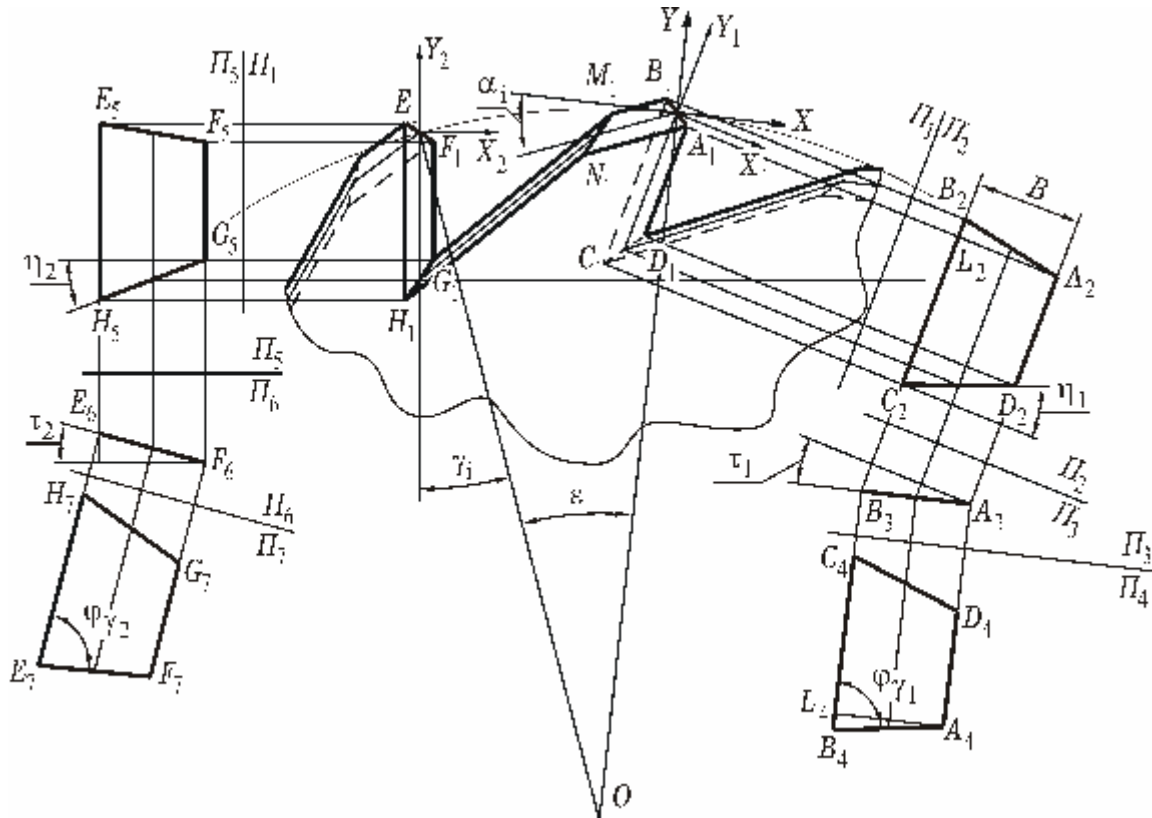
Схема різальної частини фрези з різноправленими зубцями і стружковими канавками перемінної висоти
